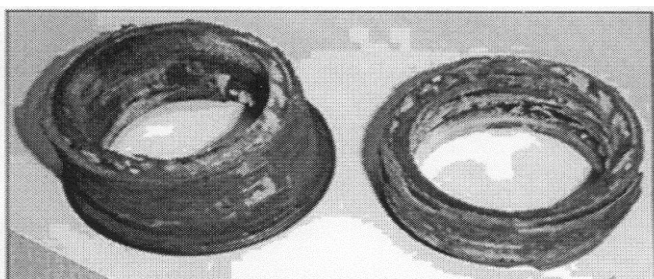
Втулка пускового подшипника после разрушения
